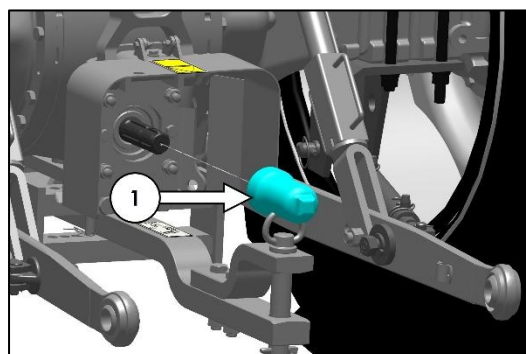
COUVERCLE ET PROTECTION DE LA PDF
